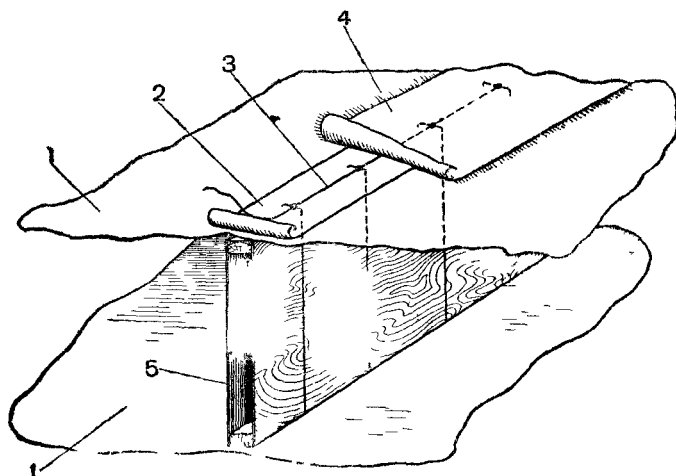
Подшивка обтяжки на крыльях и оперении:
